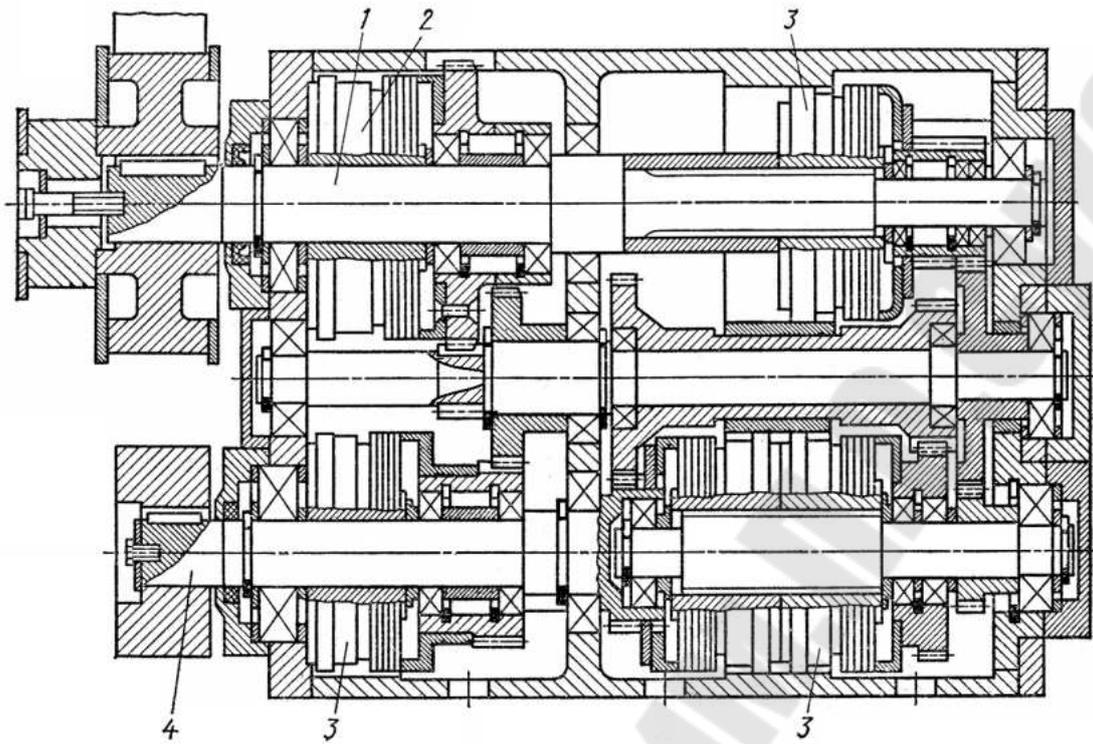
Коробка скоростей станка 1Г340П:
